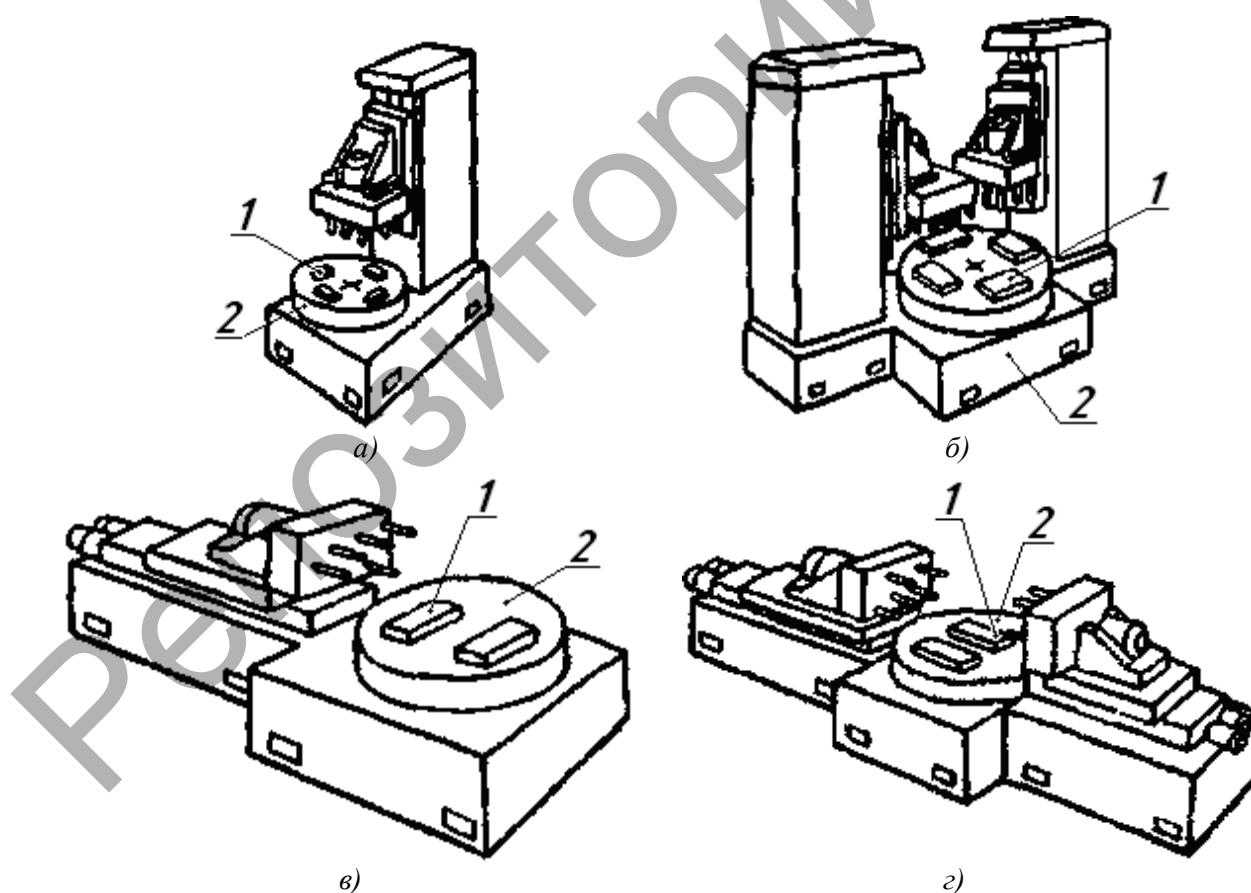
Типовые компоновки агрегатных станков с поворотным делительным столом
